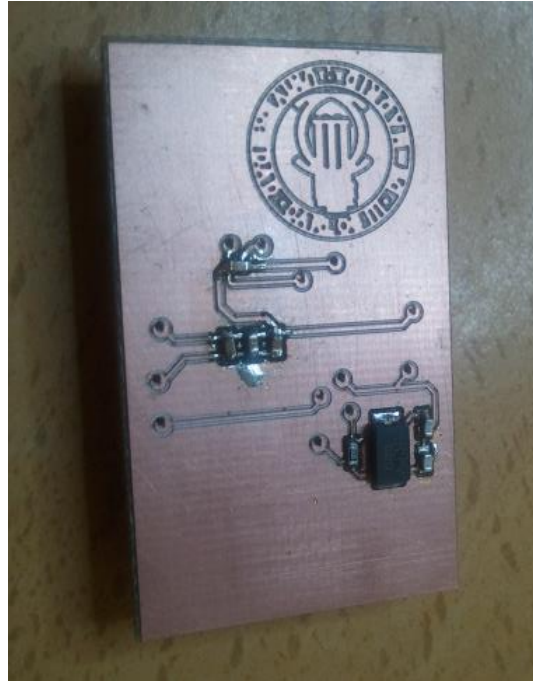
Cara Bottom Prototipo soldado manualmente
